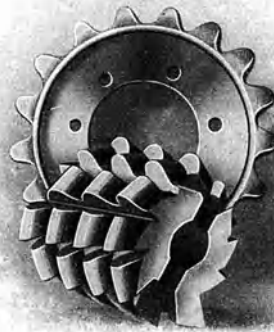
Kettenzahnrad mit dem dazu gehörigen Wälzfräser.
